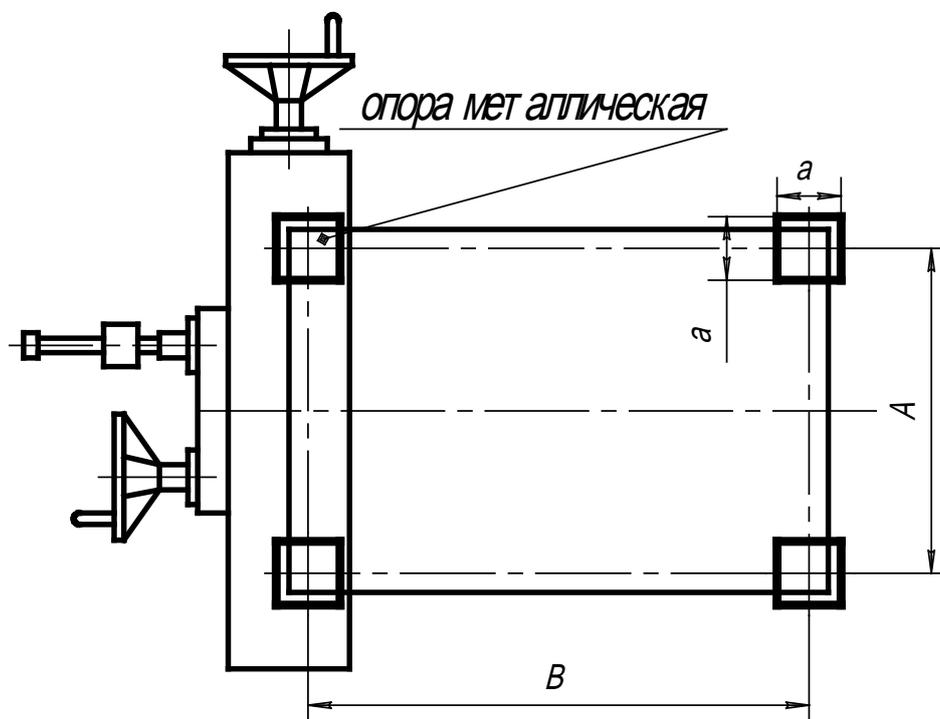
Схема расстановки опор вертикального консольно-фрезерного станка модели 6Т12-1
